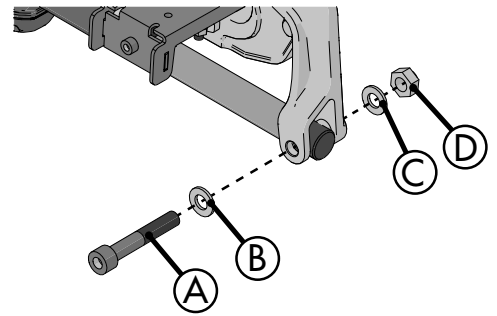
Hintere Befestigung der Stellvorrichtung.
